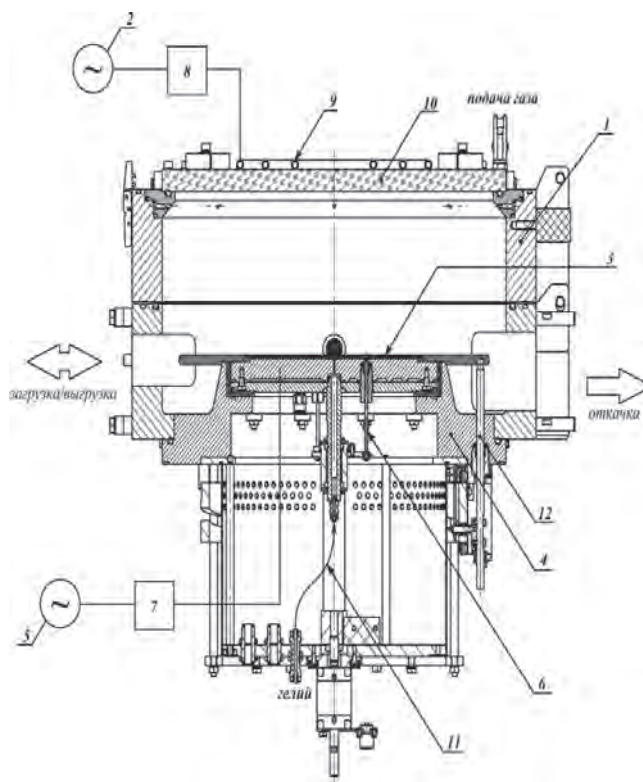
Конструкция реактора установки для травления мелкощелевой изоляции с гладкими стенками (1 — источник плазмы; 2 — ВЧ-генератор; 3 — рабочая пластина; 4 — подложкодержатель; 5 — ВЧ-генератор; 6 — механизм вертикального перемещения; 7 — устройство автоматического согласования; 8 — устройство согласования; 9 — индуктор; 10 — кварцевое окно; 11 — гелиевое охлаждение; 12 — механический прижим)
